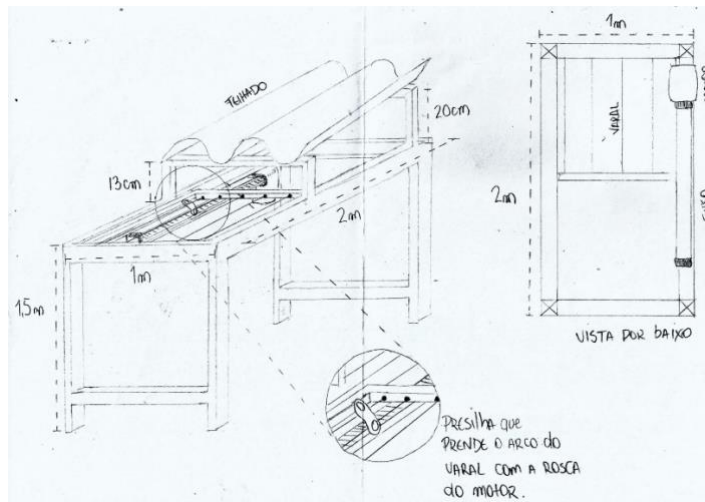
Croqui da estrutura metálica - Fonte: Próprio autor
